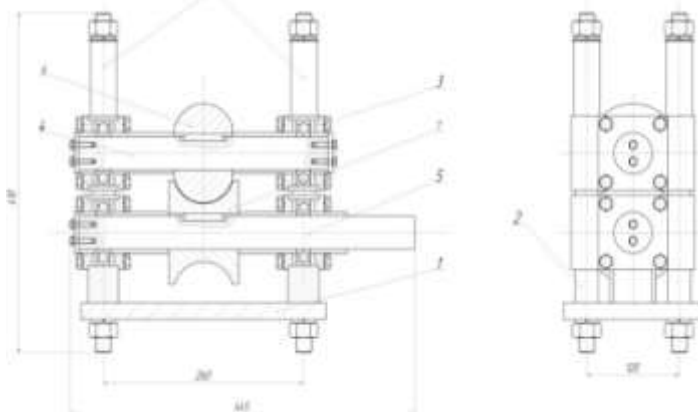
Общий вид горизонтальной рабочей клетки трубоформовочного стана: 1- станины; 2- направляющие; 3- подшипниковые подушки валов; 4- верхний вал; 5-нижний вал; 6,7-профилированные части; 8-нажимной механизм
